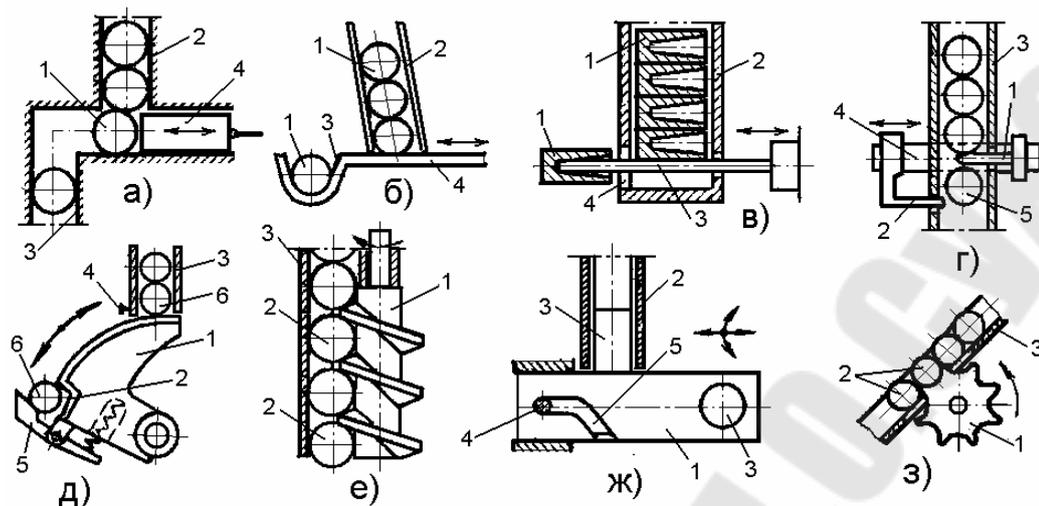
Конструктивные исполнения механизмов выдачи изделий
